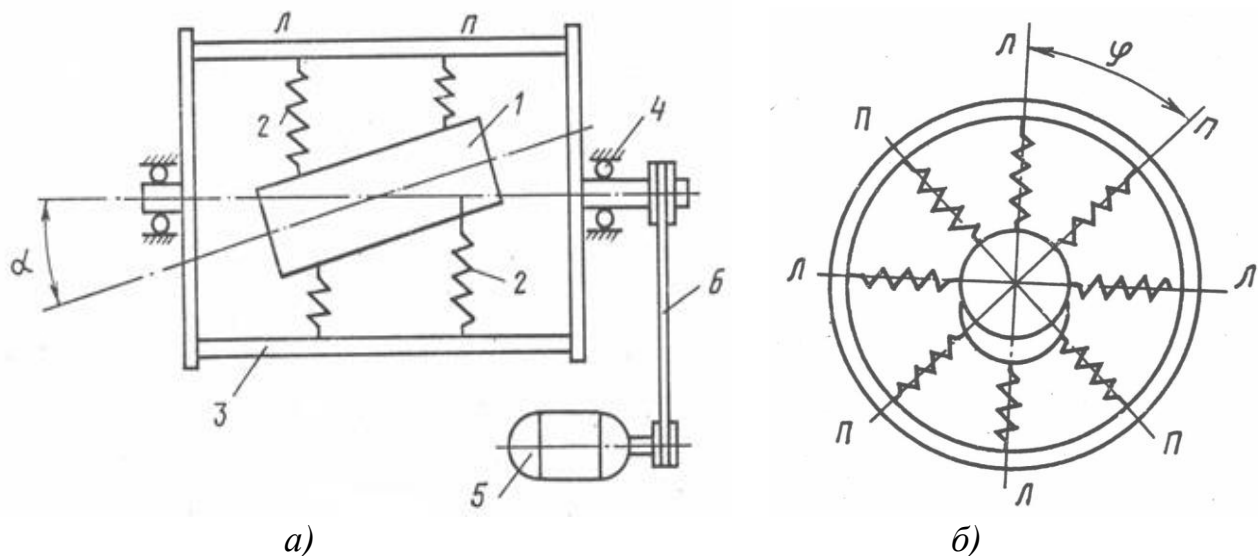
Схема машины для виброгалтовочной обработки деталей - а); схема расположения пружин его подвески относительно друг друга - б)
